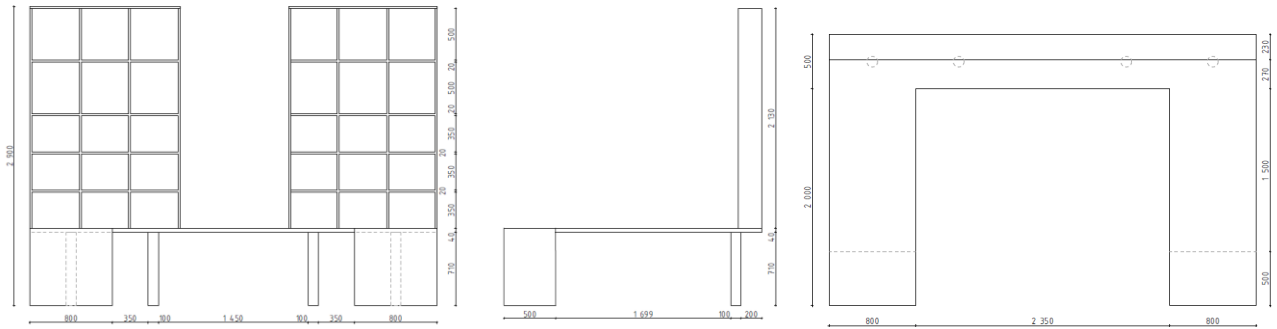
Робочий стіл. Вид спереду, вид збоку, вид зверху
